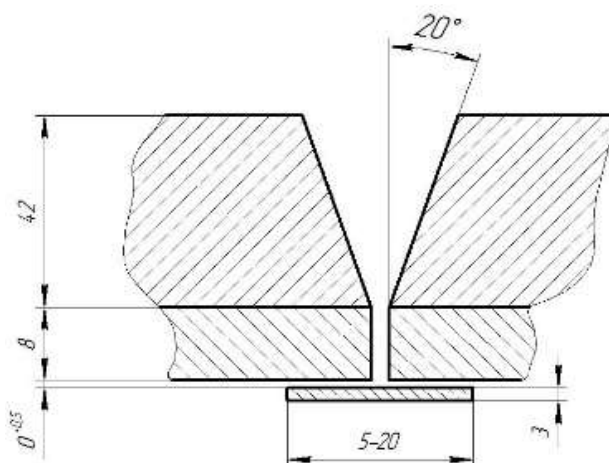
Схематичне вигляд розроблення кромки, та геометричні розміри зварного з'єднання
